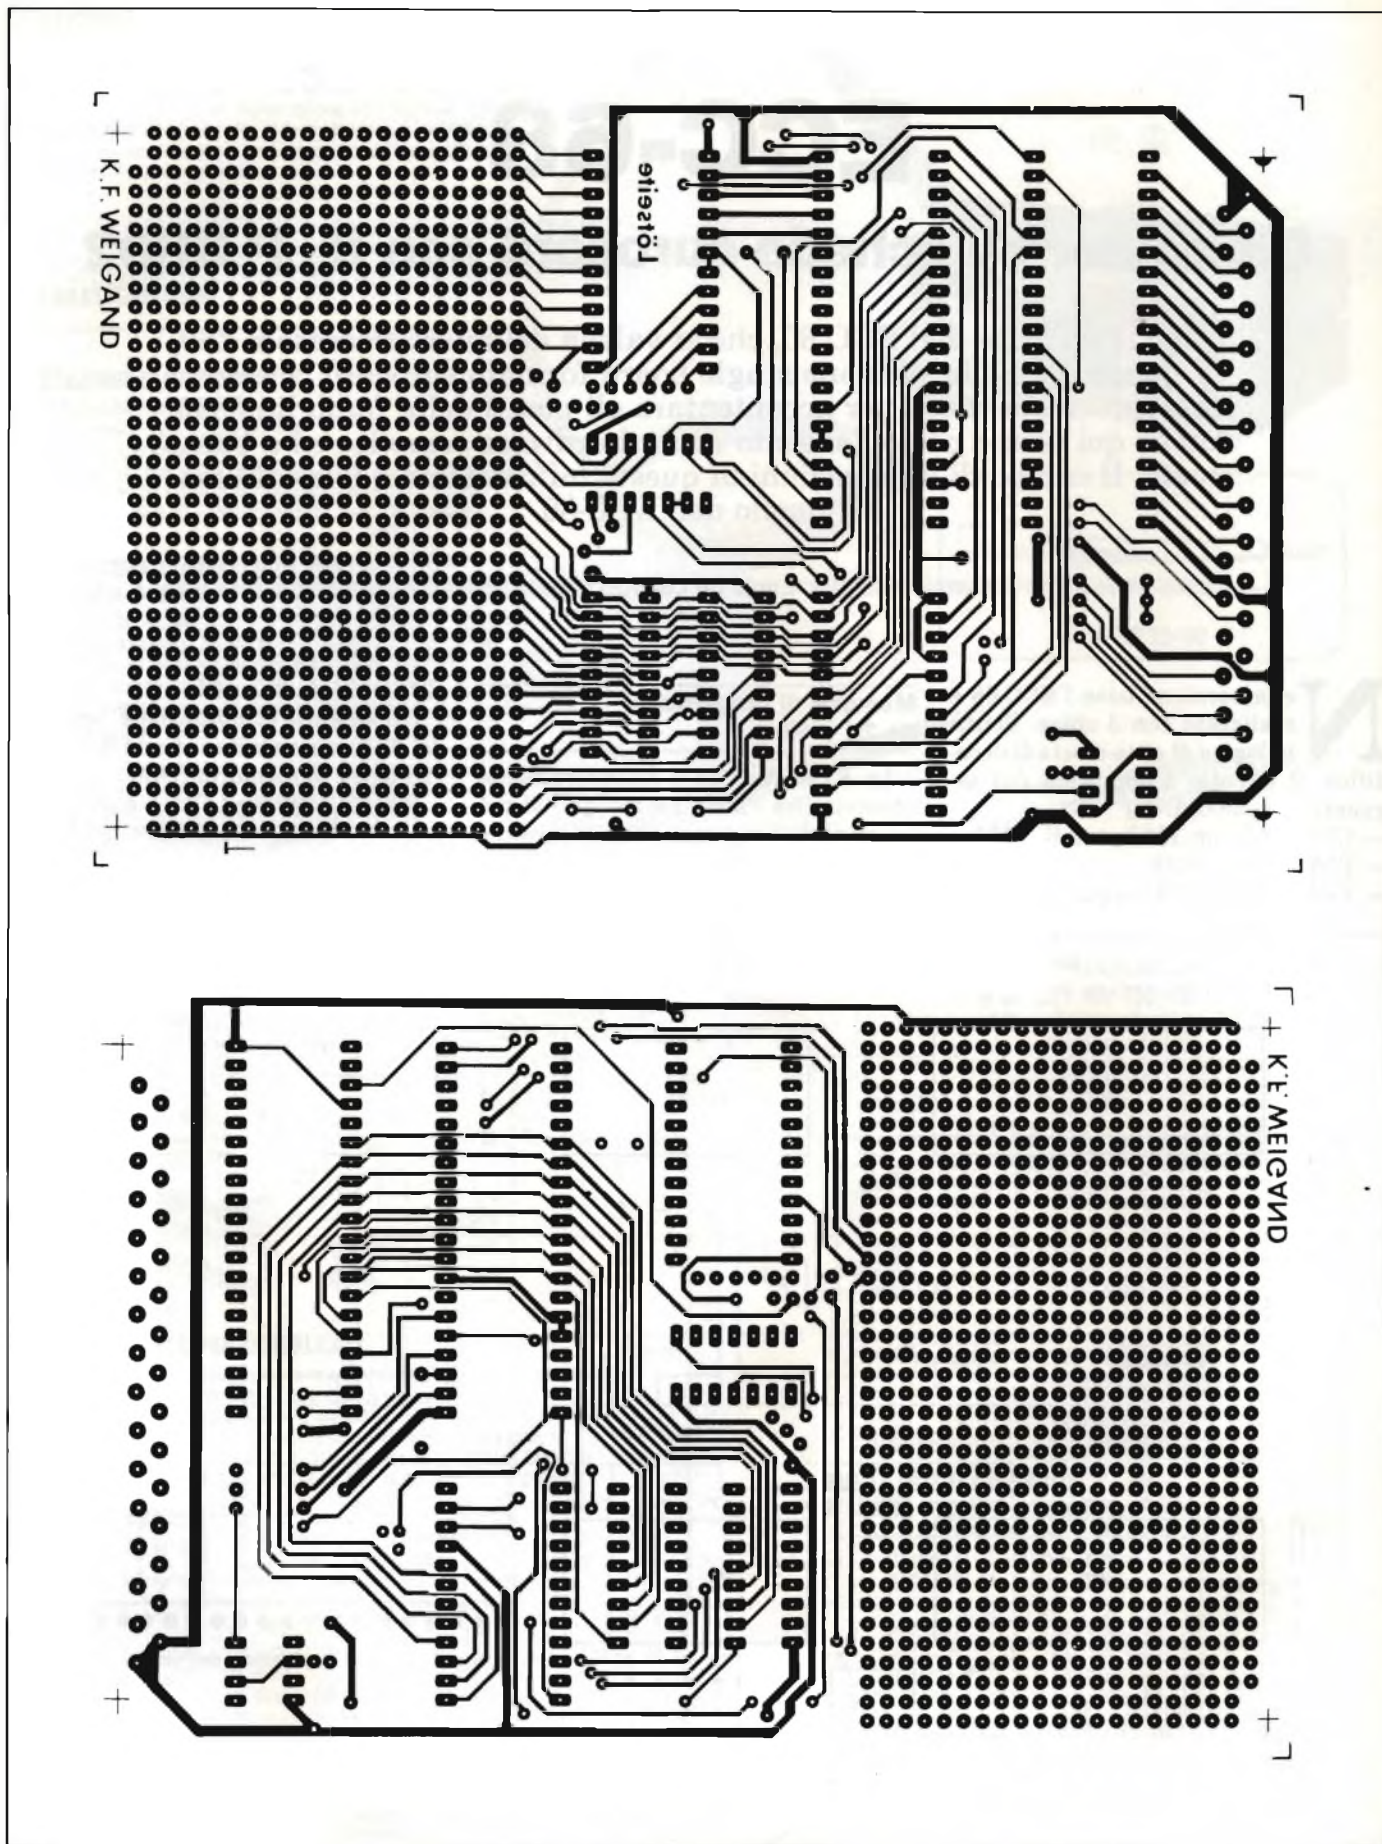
Il layout della scheda. A destra il lato componenti, a sinistra il lato saldature.
